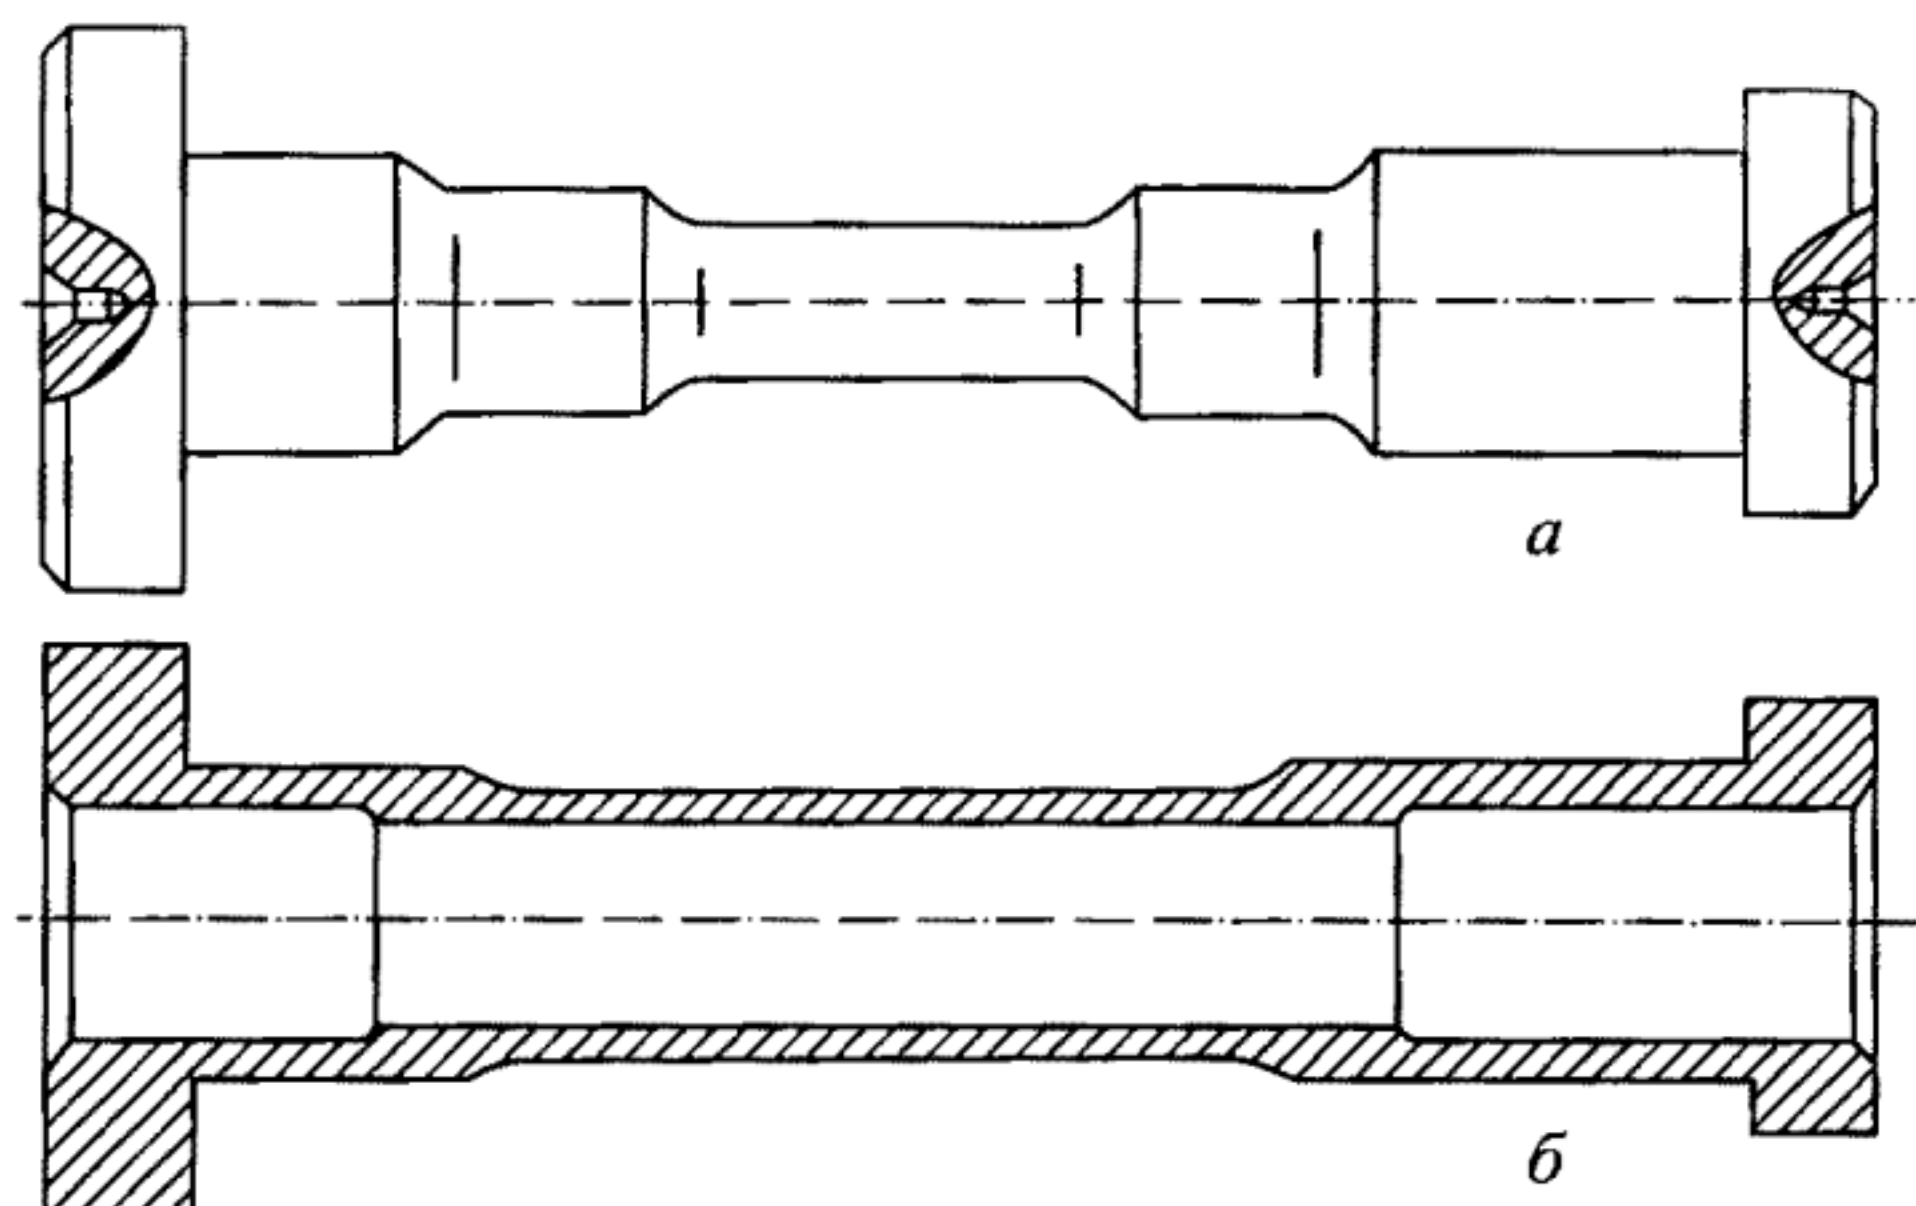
Сплошной (а) и трубчатый (б) типы цилиндрических образцов для испытаний
